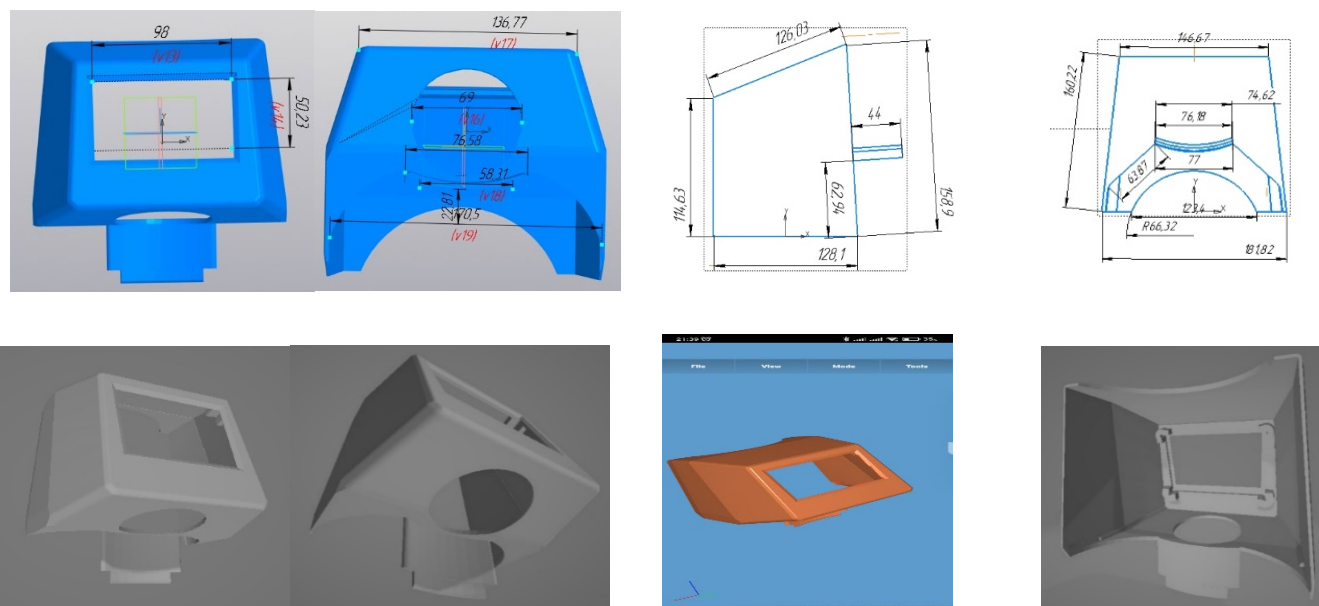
Основні розміри корпусу та підготовленої 3D моделі для виготовлення
